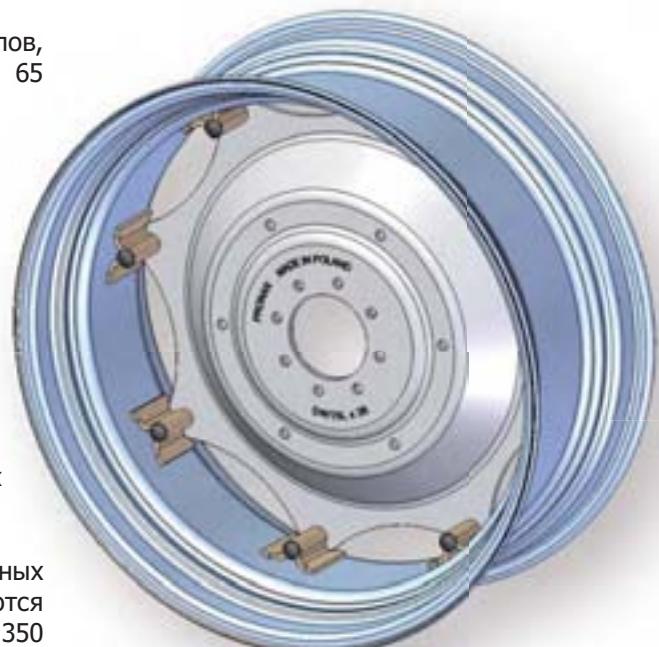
Колеса для сельскохозяйственных тракторов, свинчивающаяся версия с захватами типа „омега”
